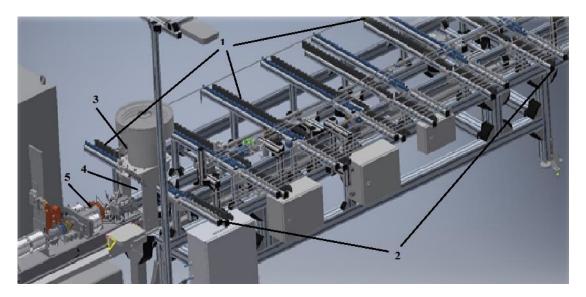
внешний вид установки контактно-стыковой сварки Установка состоит из следующих элементов:
